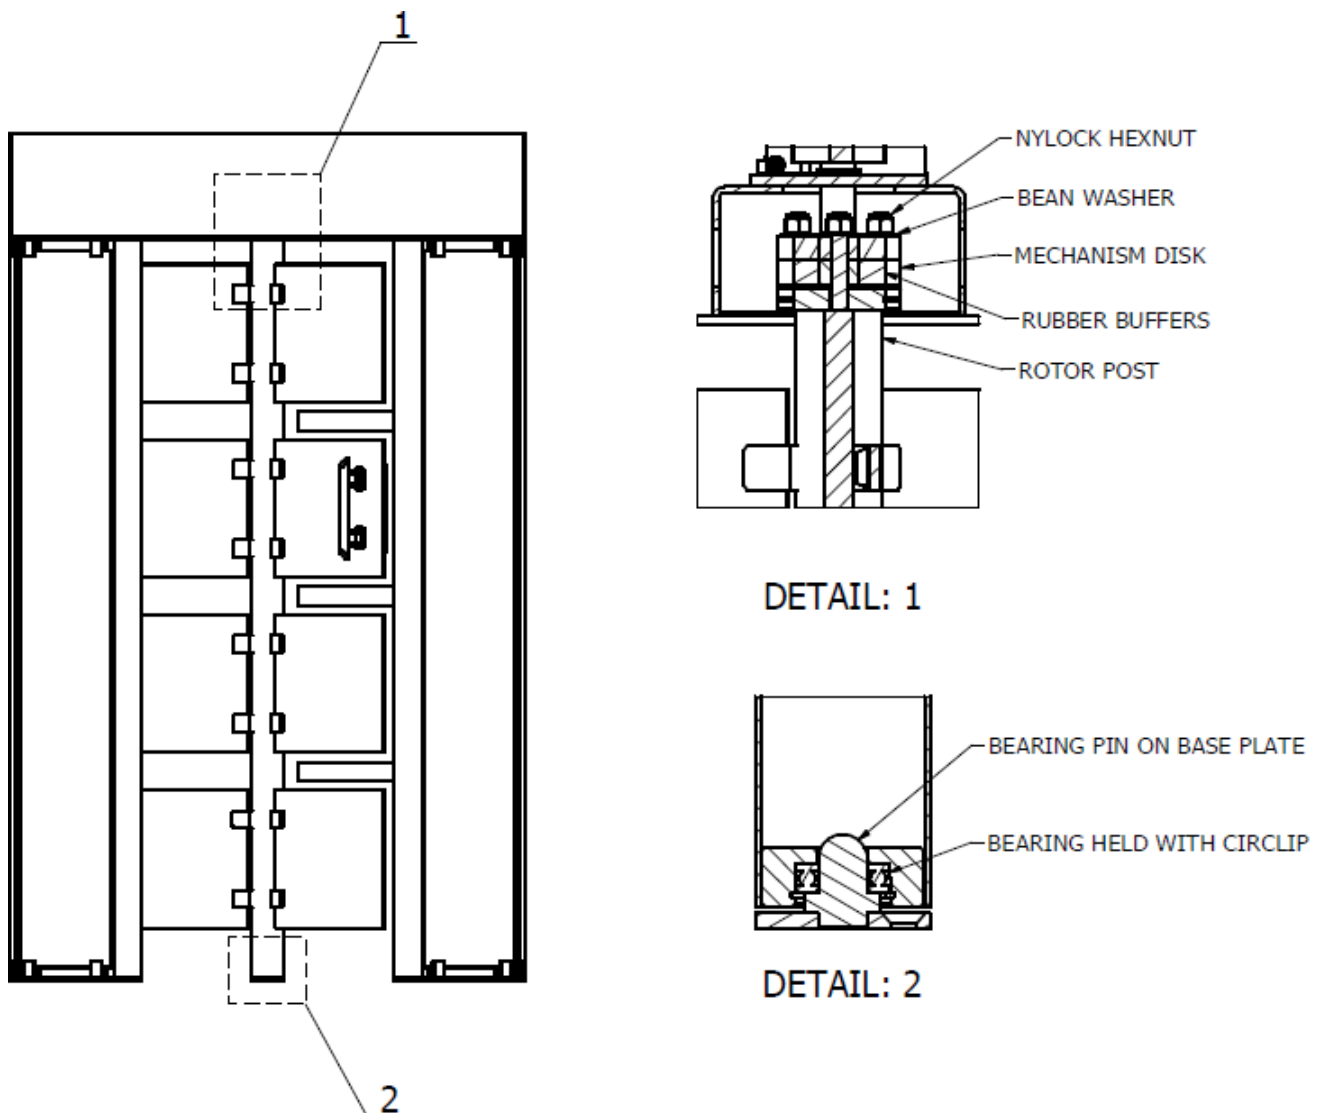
Platzierung der Teile für die Rotorbaugruppe
